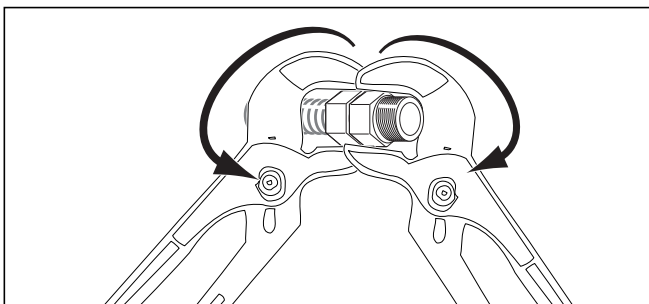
Doppelnippel zum Stauchen des Rohrendes fest einschrauben. Dazu die beiden Fittings mit einem Zangenschlüssel halten und die Verschraubung kräftig zudrehen. Nicht in Schraubstock spannen!
